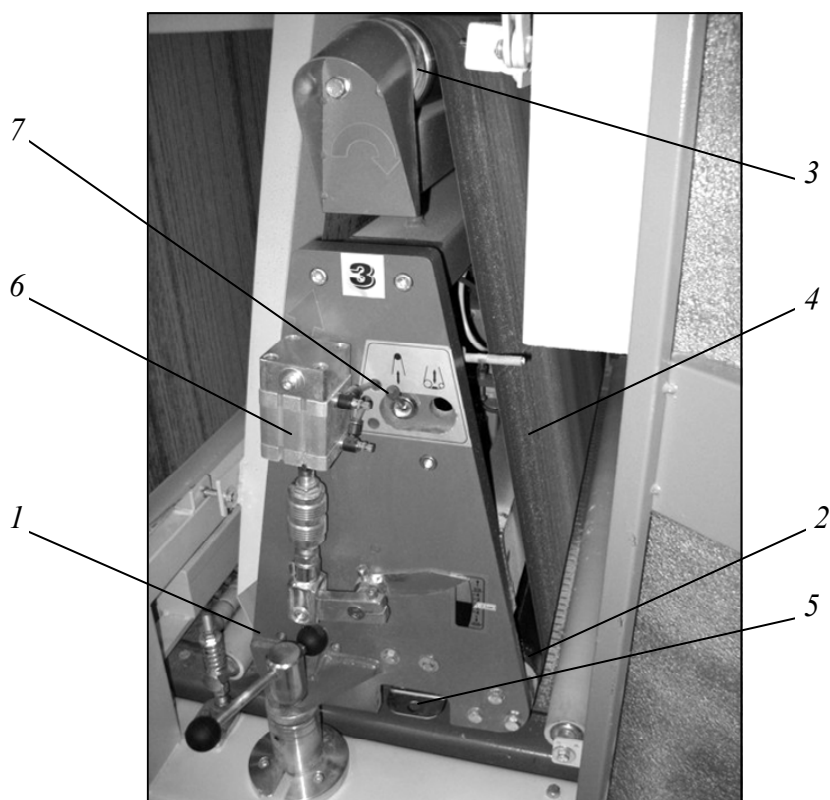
Шлифовальный узел С широколенточного фрезерно-шлифовального станка Houfek Bulldog FRC 910
